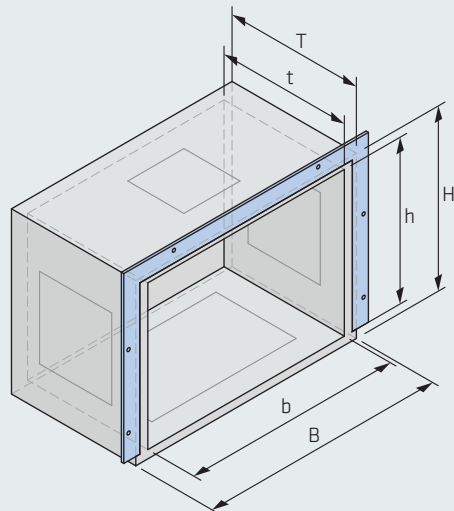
Schall-ISOBX TSB-MB (стіни з кам'яної кладки та бетону)
